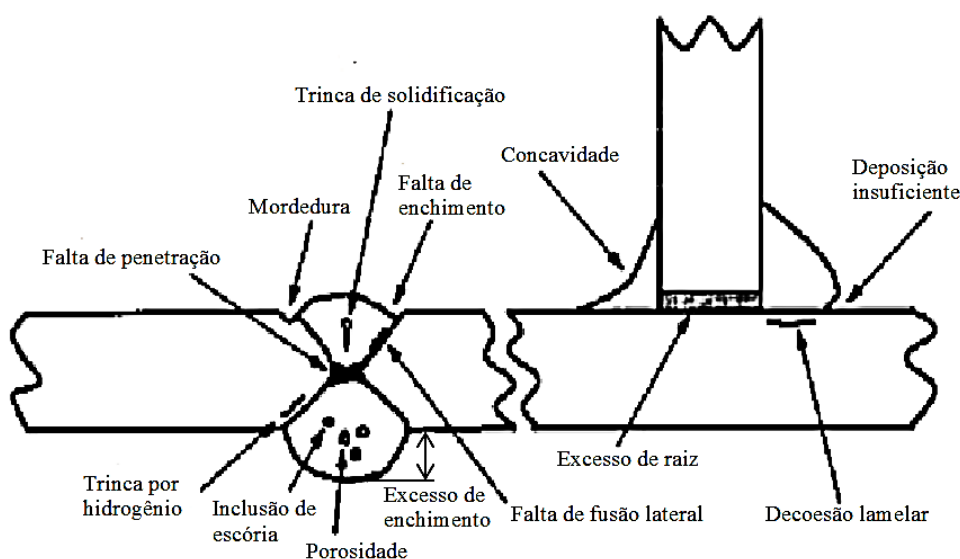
Defeitos encontrados em juntas soldadas.
